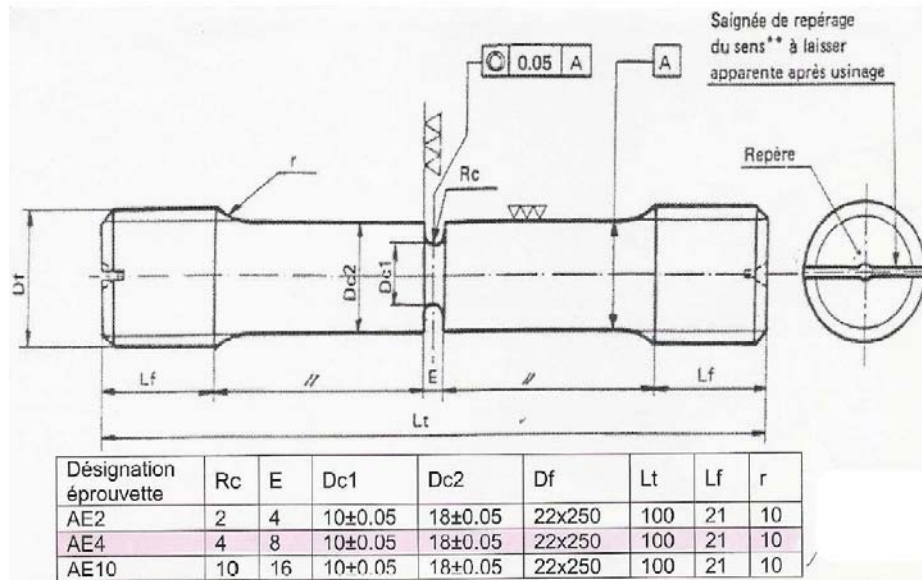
Plan de définition des éprouvettes axisymétriques entaillées
